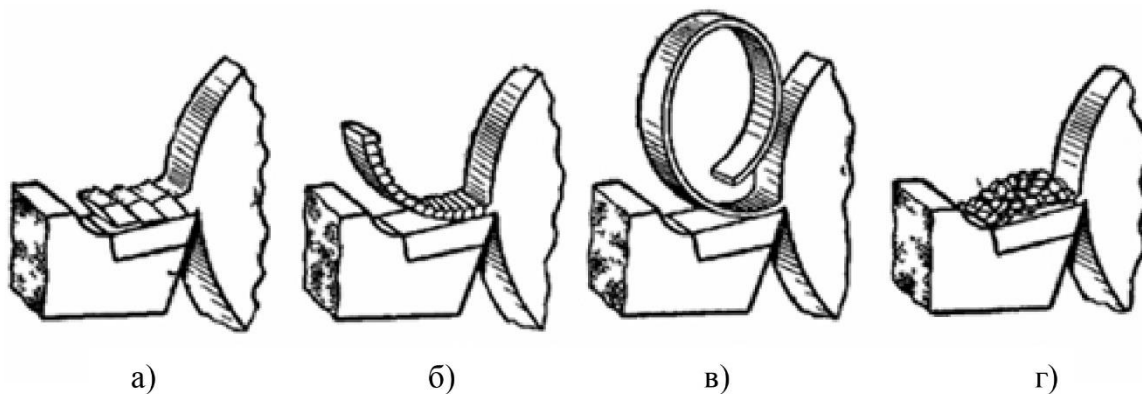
Типы стружек, образующихся при резании металлов: а – сливная; б – элементная; в – суставчатая; г – надлома [26-28]
